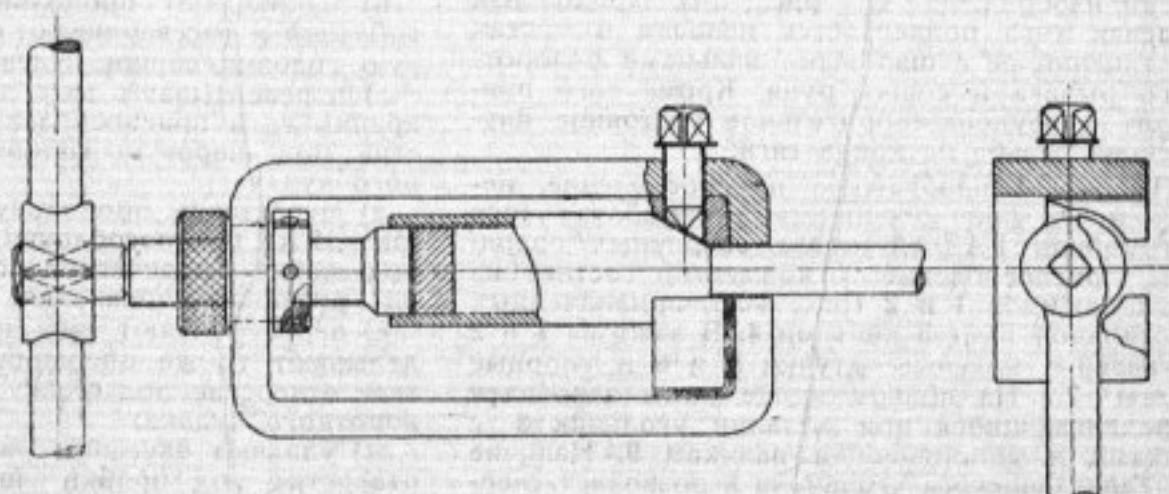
Приспособление для вывертывания старых пробок рулевых тяг
